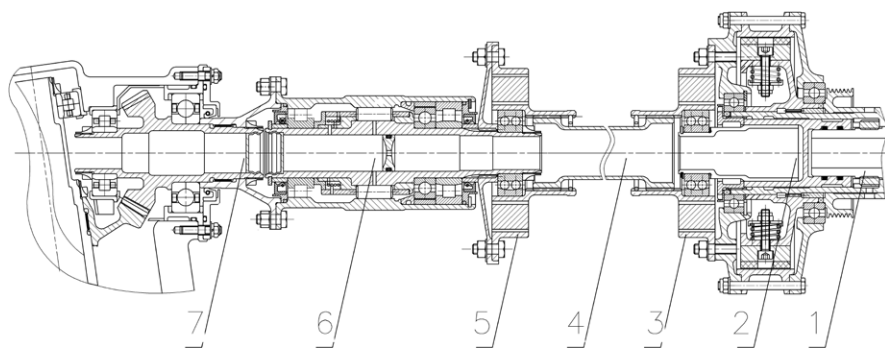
Участок трансмиссии от двигателя к главному редуктору: 1 – коленвал двигателя; 2 – автоматическая муфта включения; 3 – упругая компенсирующая муфта; 4 – вал-рессора; 5 – упругая компенсирующая муфта; 6 – муфта свободного хода; 7 – главный редуктор.
